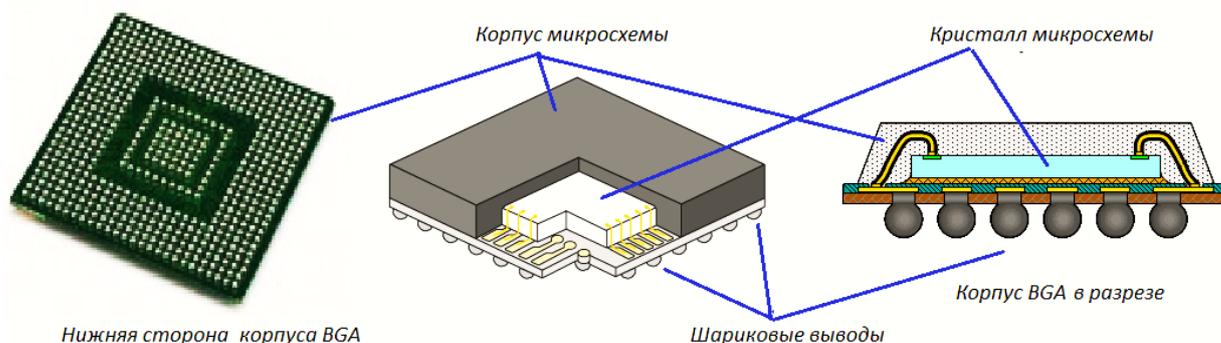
Микросхема в матричном корпусе с выводами BGA
